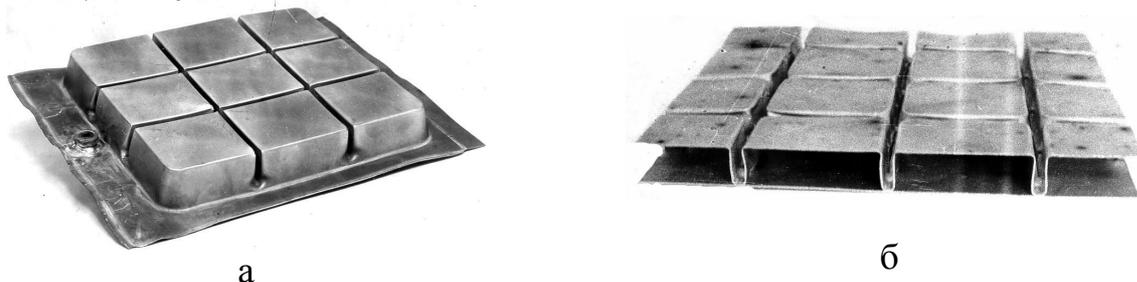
Формованный ячеистый наполнитель из алюминиевого АМг6 (а) и титанового ВТ6С (б) сплавов
